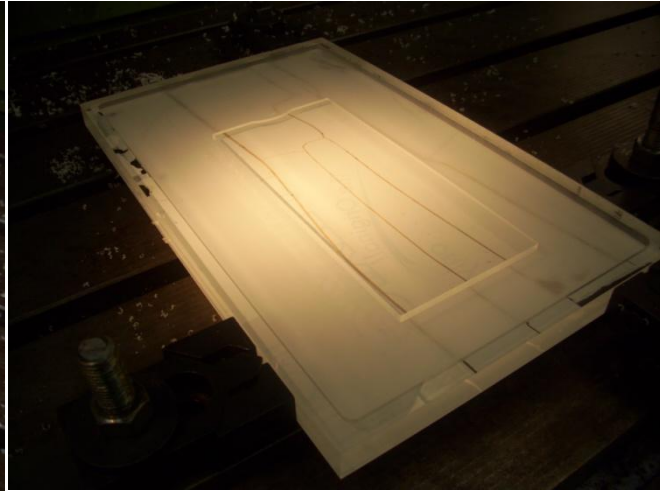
Detalle de la isla mecanizada con el rebaje.
